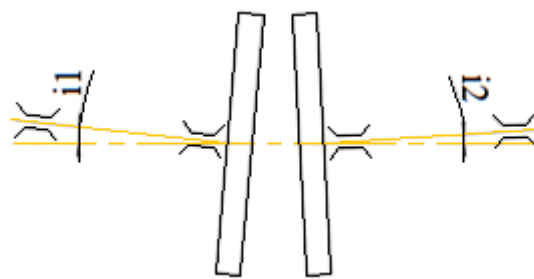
Расположение фрез под углом при наличии имеющихся зазоров в подшипниковых опорах под воздействием силы резания и нежёсткости корпусов фрез
